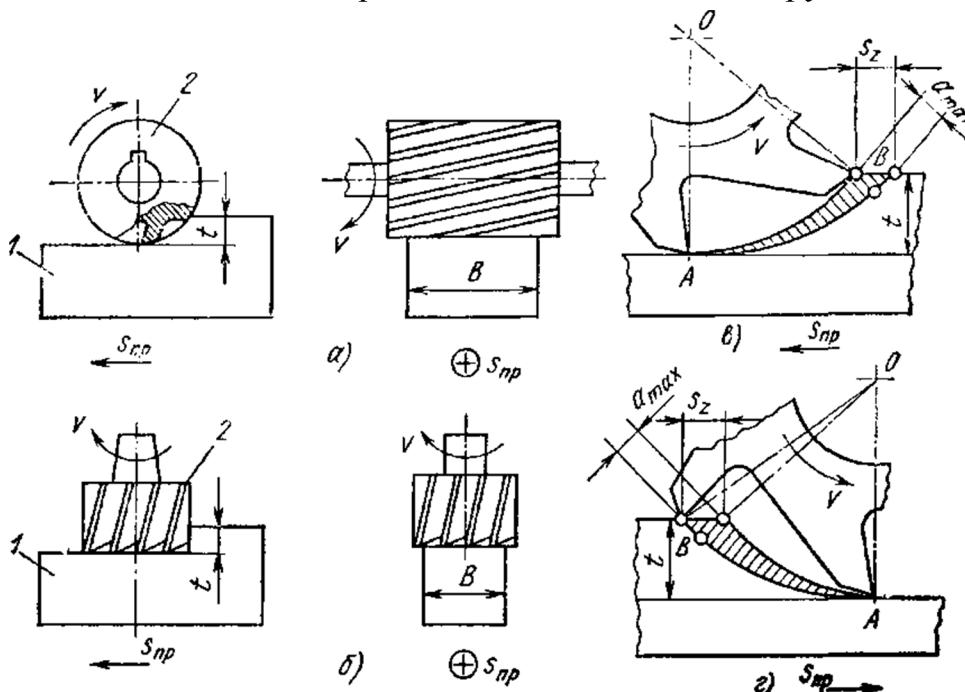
Схемы фрезерования цилиндрической (а) и торцовой (б) фрезами, встречного (в) и попутного (г) фрезерования:
